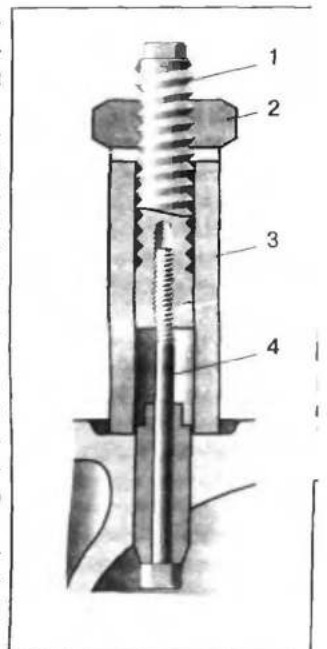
Винтовое приспособление для выпрессовки направляющих втулок: 1 — винт; 2 — гайка; 3 — стержень; 4 — болт
